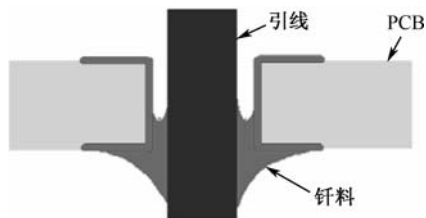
PCB 浸入钎料波峰太浅造成透孔不良
